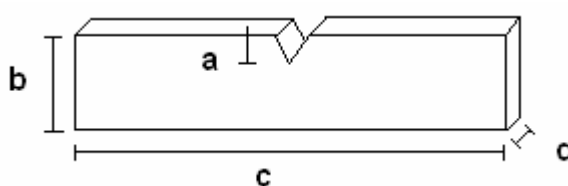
Dimensões do corpo de prova para ensaio de impacto instrumentado izod: a) profundidade do entalhe (2,54 mm); b) largura (11,00 mm); c) comprimento (55,00 mm) e d) espessura (1,50 mm).
